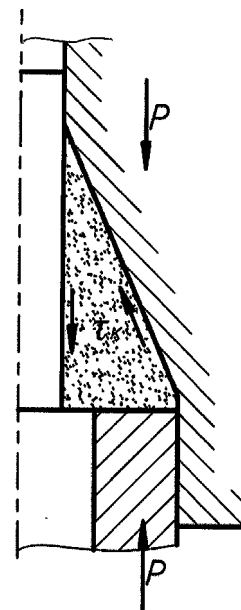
Схема действия касательных напряжений τ_k при формировании порошковой шихты
